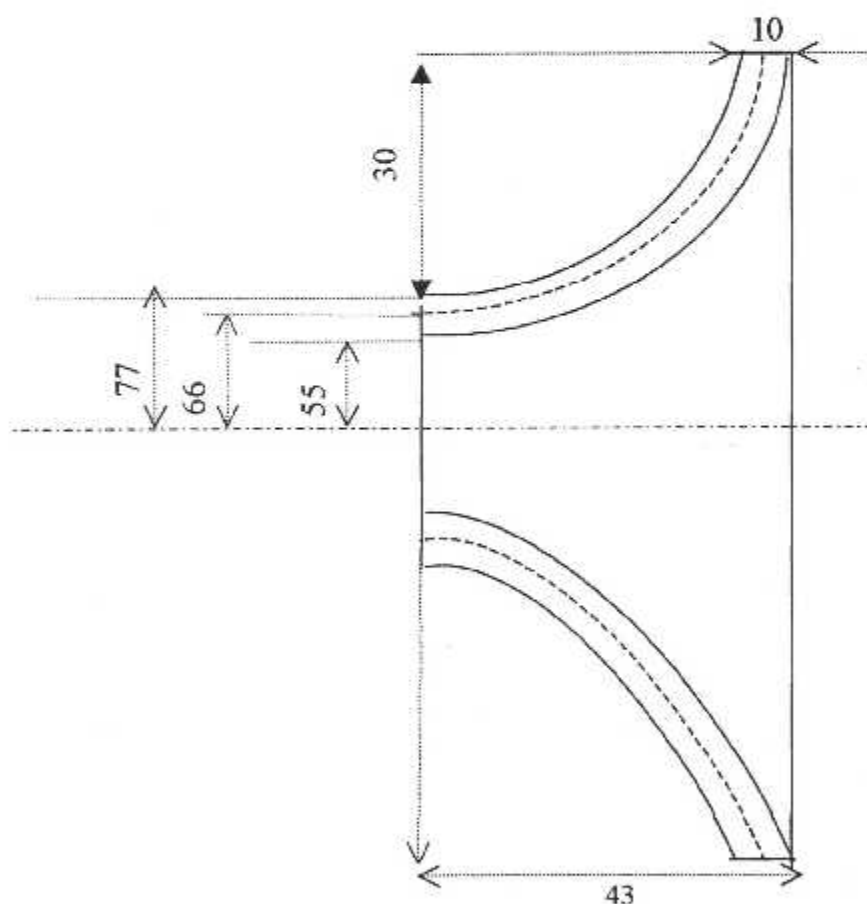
Dimensions de la rouet du compresseur centrifuge
